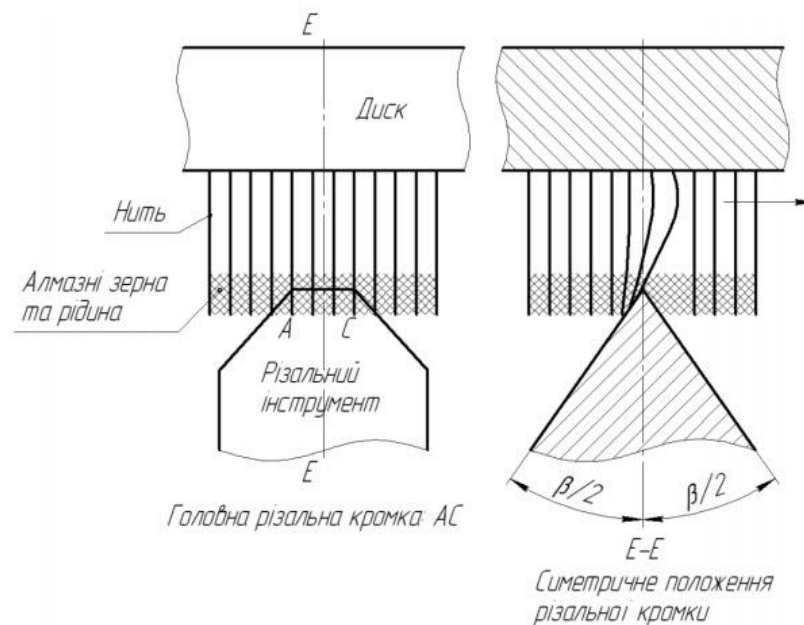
Схема оброблення РК інструменту абразивними щітками
